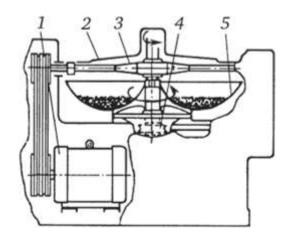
Устройство базового промышленного куттера: 1— электродвигатель; 2— крышка; 3— ножевой вал; 4— червячная передача; 5— чаша
